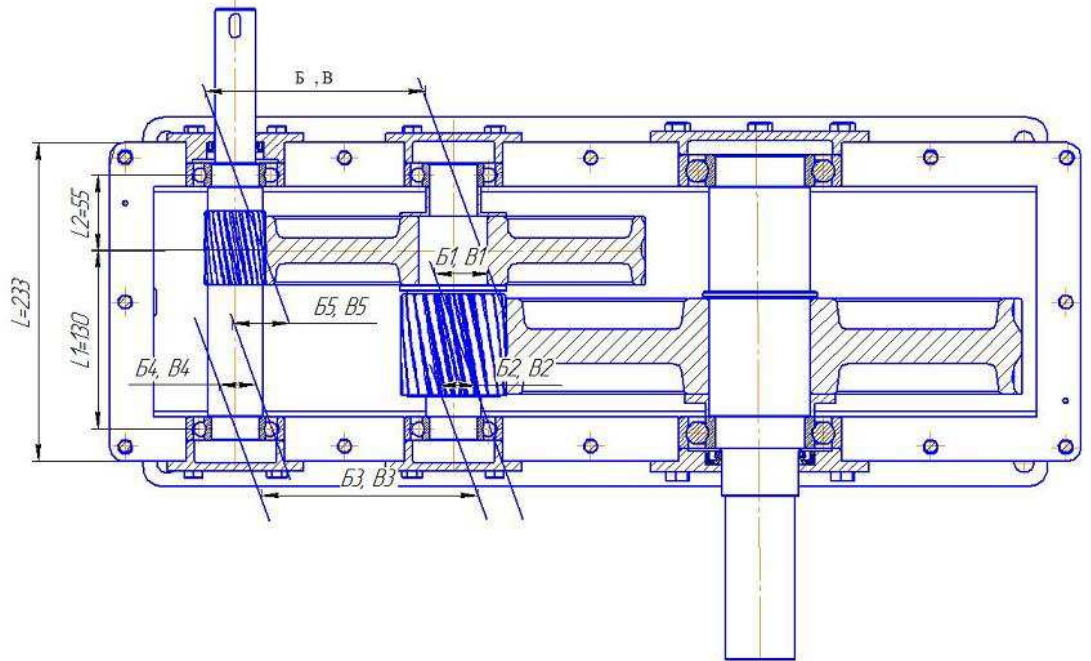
Размерные цепи цилиндрической зубчатой передачи
